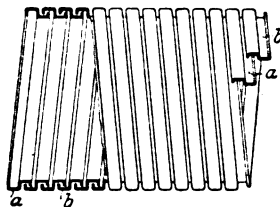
Schlauch mit mehrgängigem Gewinde.
